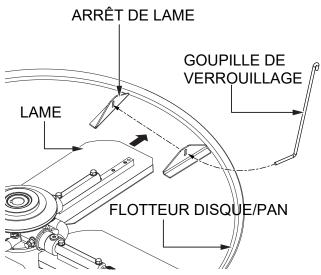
Pan flotteur Installation (Goupilles de verrouillage)
